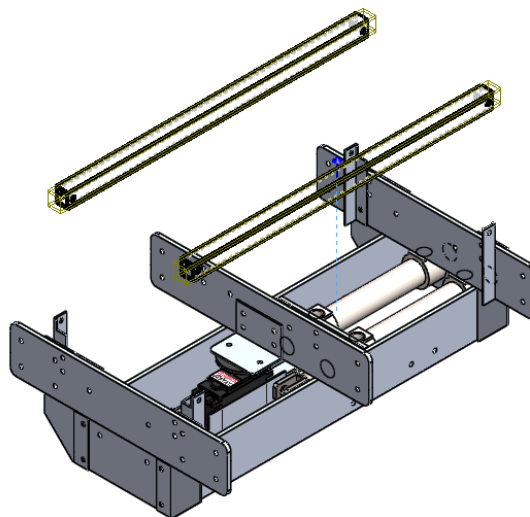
Ensamble placa principal de giro en la estructura del robot
